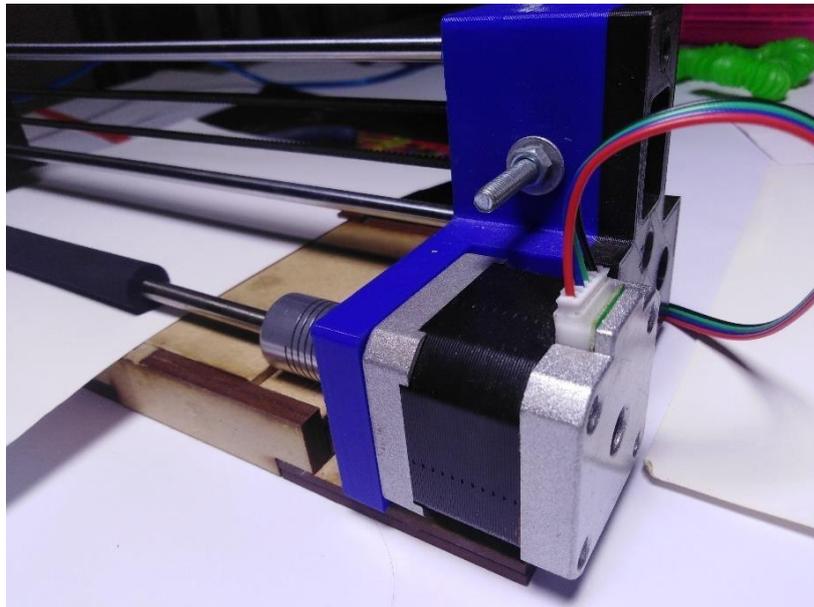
Instalación de motor sobre soporte izquierdo. Elaborado por el autor
